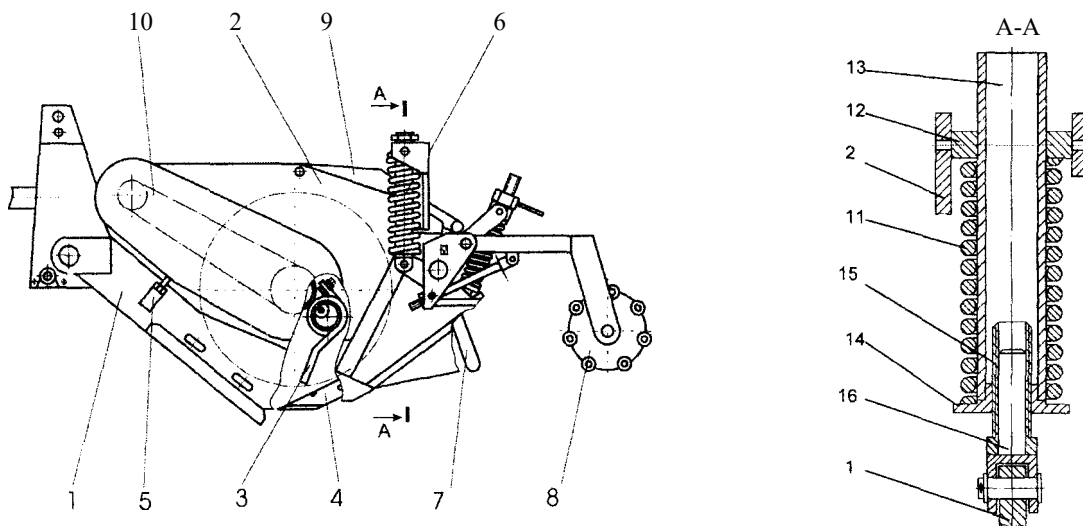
Конструктивная схема агрегата комбинированного почвообрабатывающего ПАН-3
